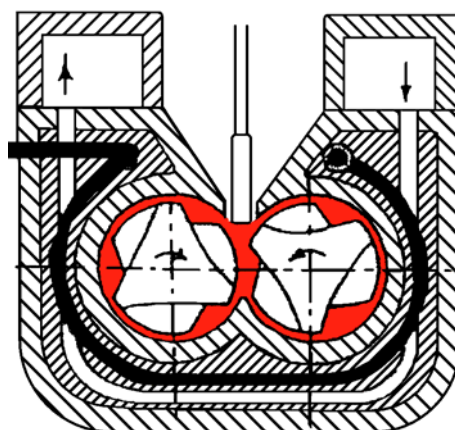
Vue en coupe du Rheomix 600, chambre de mélangeage en rouge
